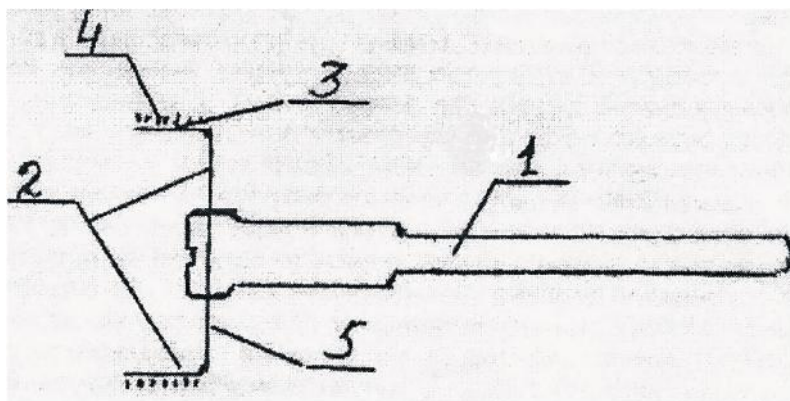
Абразивний інструмент (Схематично загальний вигляд) де:
